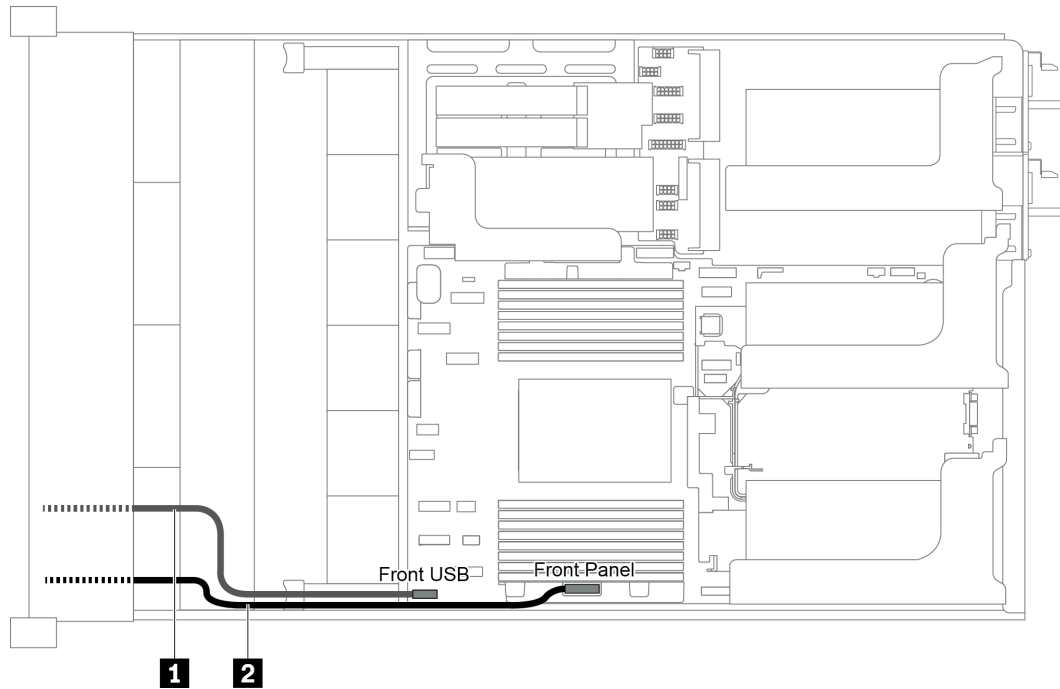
Roteamento de cabos do conjunto de E/S frontal no chassi
